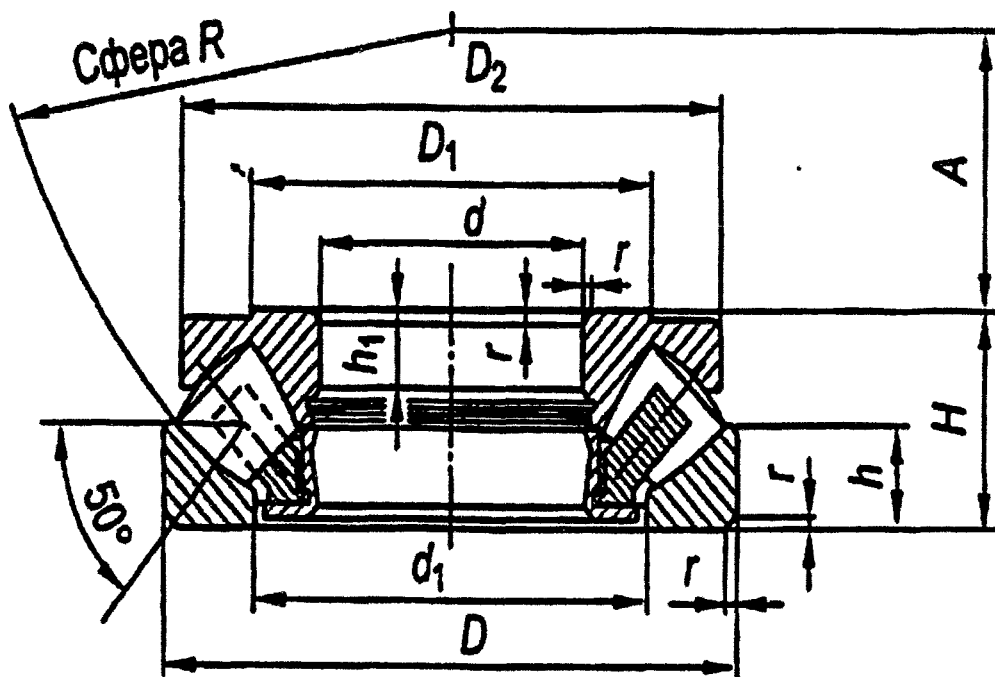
Подшипник роликовый упорно-радиальный сферический исполнения 39 000
